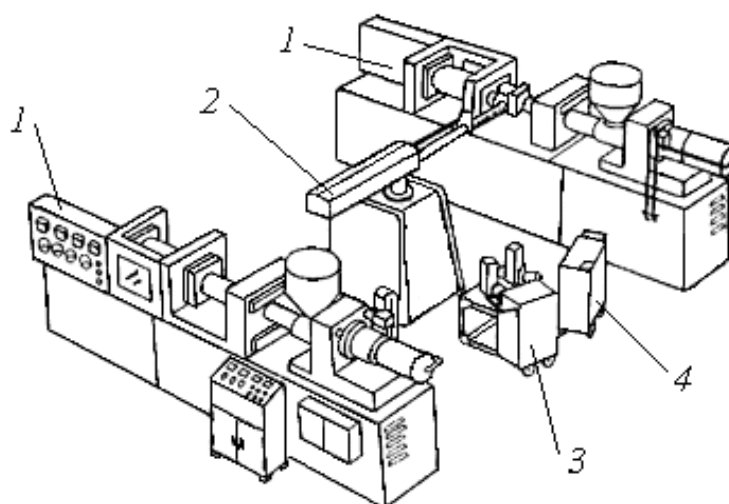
Схема РТК из двух пресслитевых машин для производства деталей из пластмасс:
